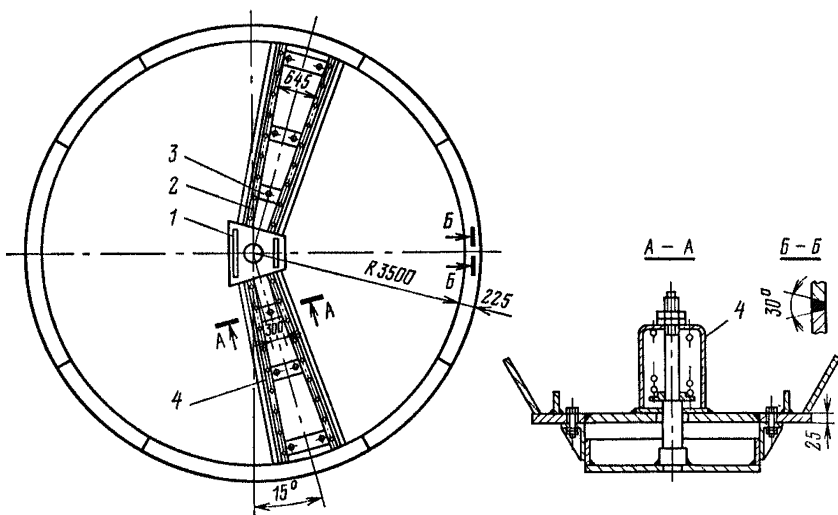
Опорные конструкции для установки новых секторных плит.
